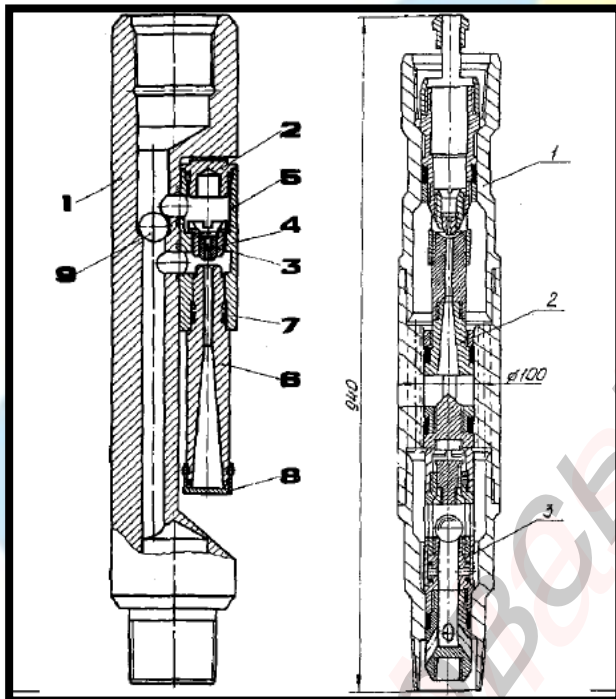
Пристрій для обробки свердловин УОС-1:
